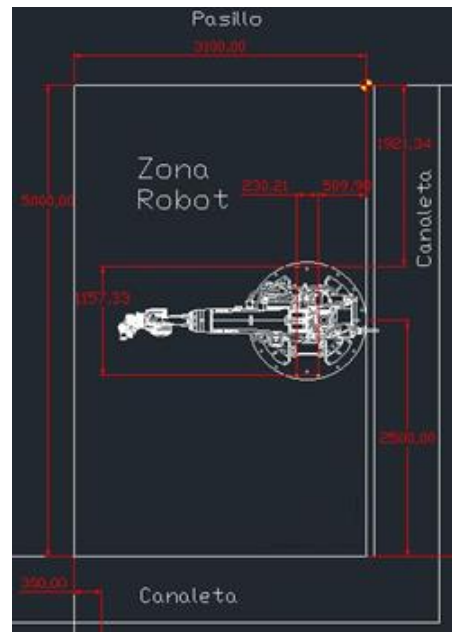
2 Dimensiones de la célula de soldadura
